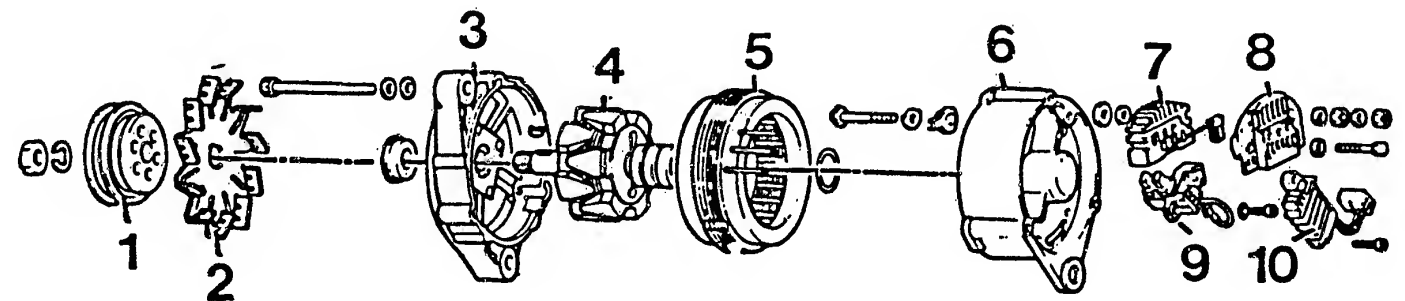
Generator M. Marelli AA 125 E-14 V: 1 Riemenscheibe – 2 Ventilator – 3 Gehäuse vorn – 4 Rotor – 5 Stator – 6 Gehäuse hinten – 7 Diodenträger – 8 Abdeckung – 9 Kohlebürsten – 10 Regler.
